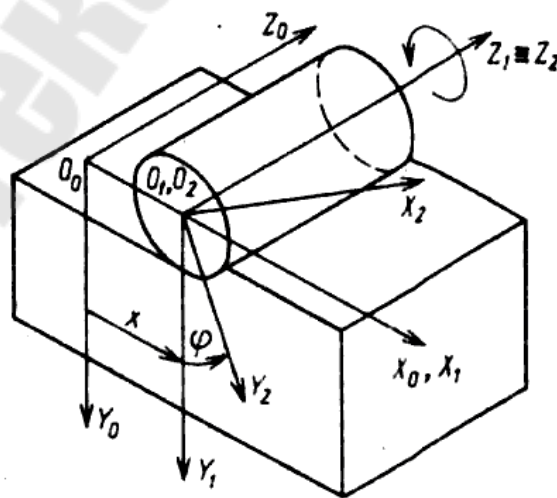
Схема фрезерования плоскости цилиндрической фрезой
